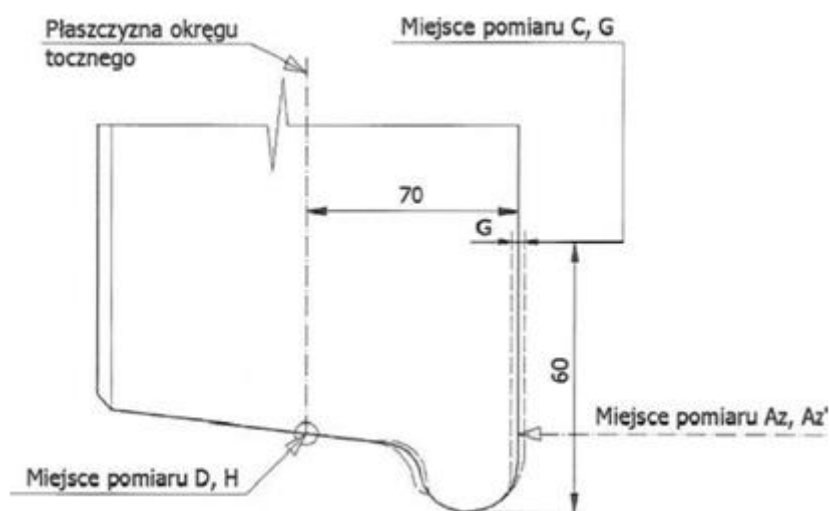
Oznaczenia elementów zarysu zewnętrznego zestawu kołowego.
